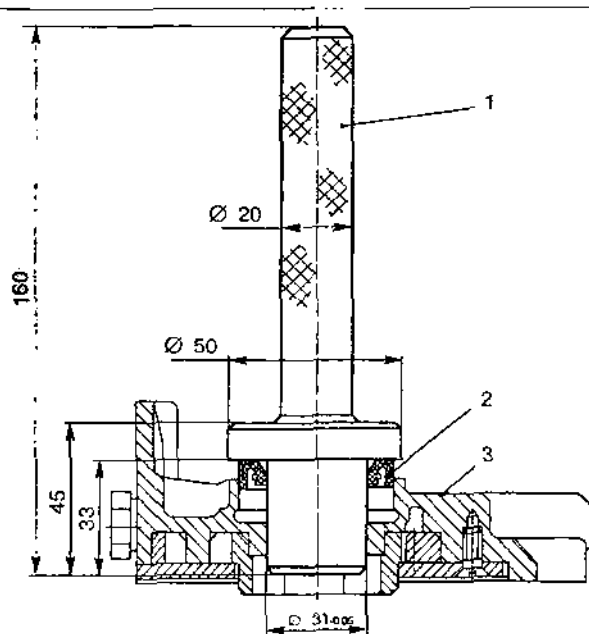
Запрессовка манжеты в корпус масляного насоса: 1 - оправка М9840-879; 2 - манжета; 3 - корпус масляного насоса.
